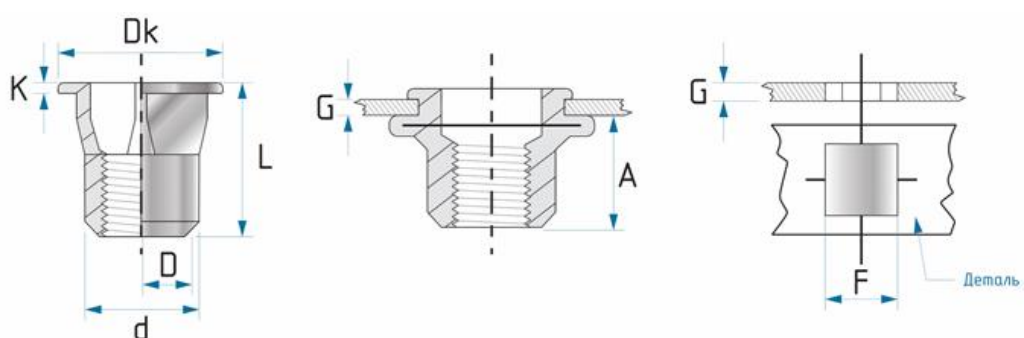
Заклёпка резьбовая квадратная, стандартный борт
